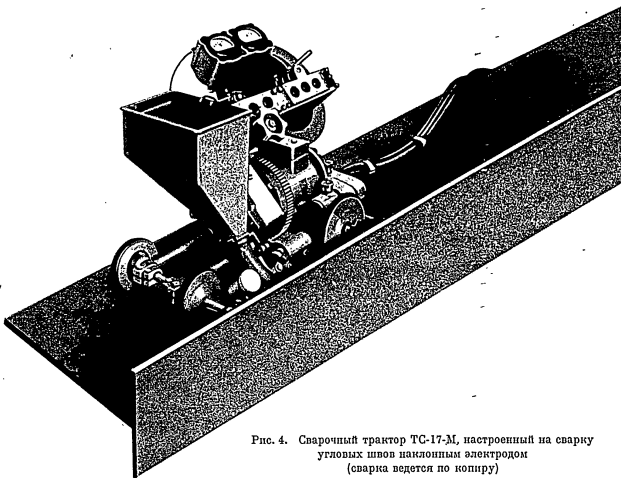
Сварочный трактор TC-17-M, настроенный на сварку угловых швов наклонным электродом (сварка ведется по копиру)
